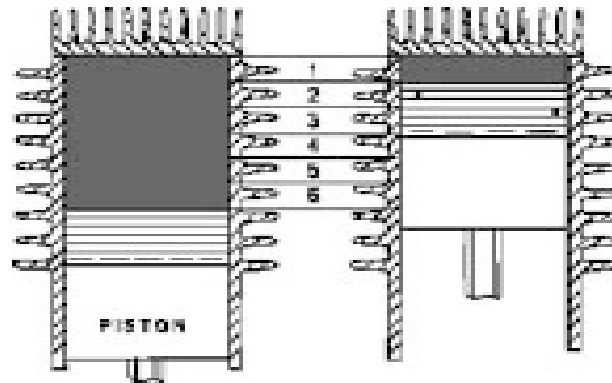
Motor de combustión con relación de compresión de seis a uno.
